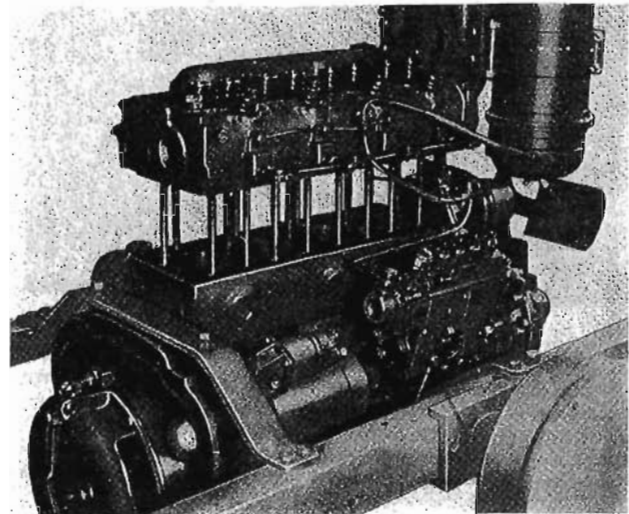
Stacco della testa cilindri completa di filtro aria.
